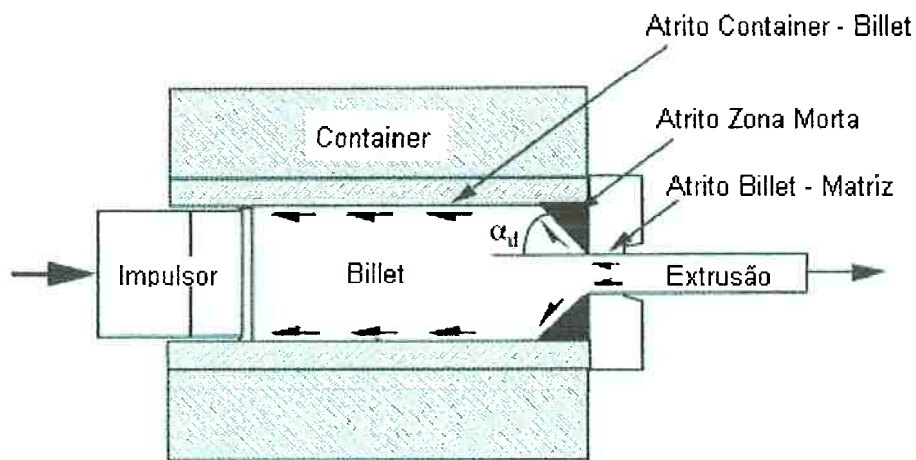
Componentes de atrito durante a extrusão^[1].
